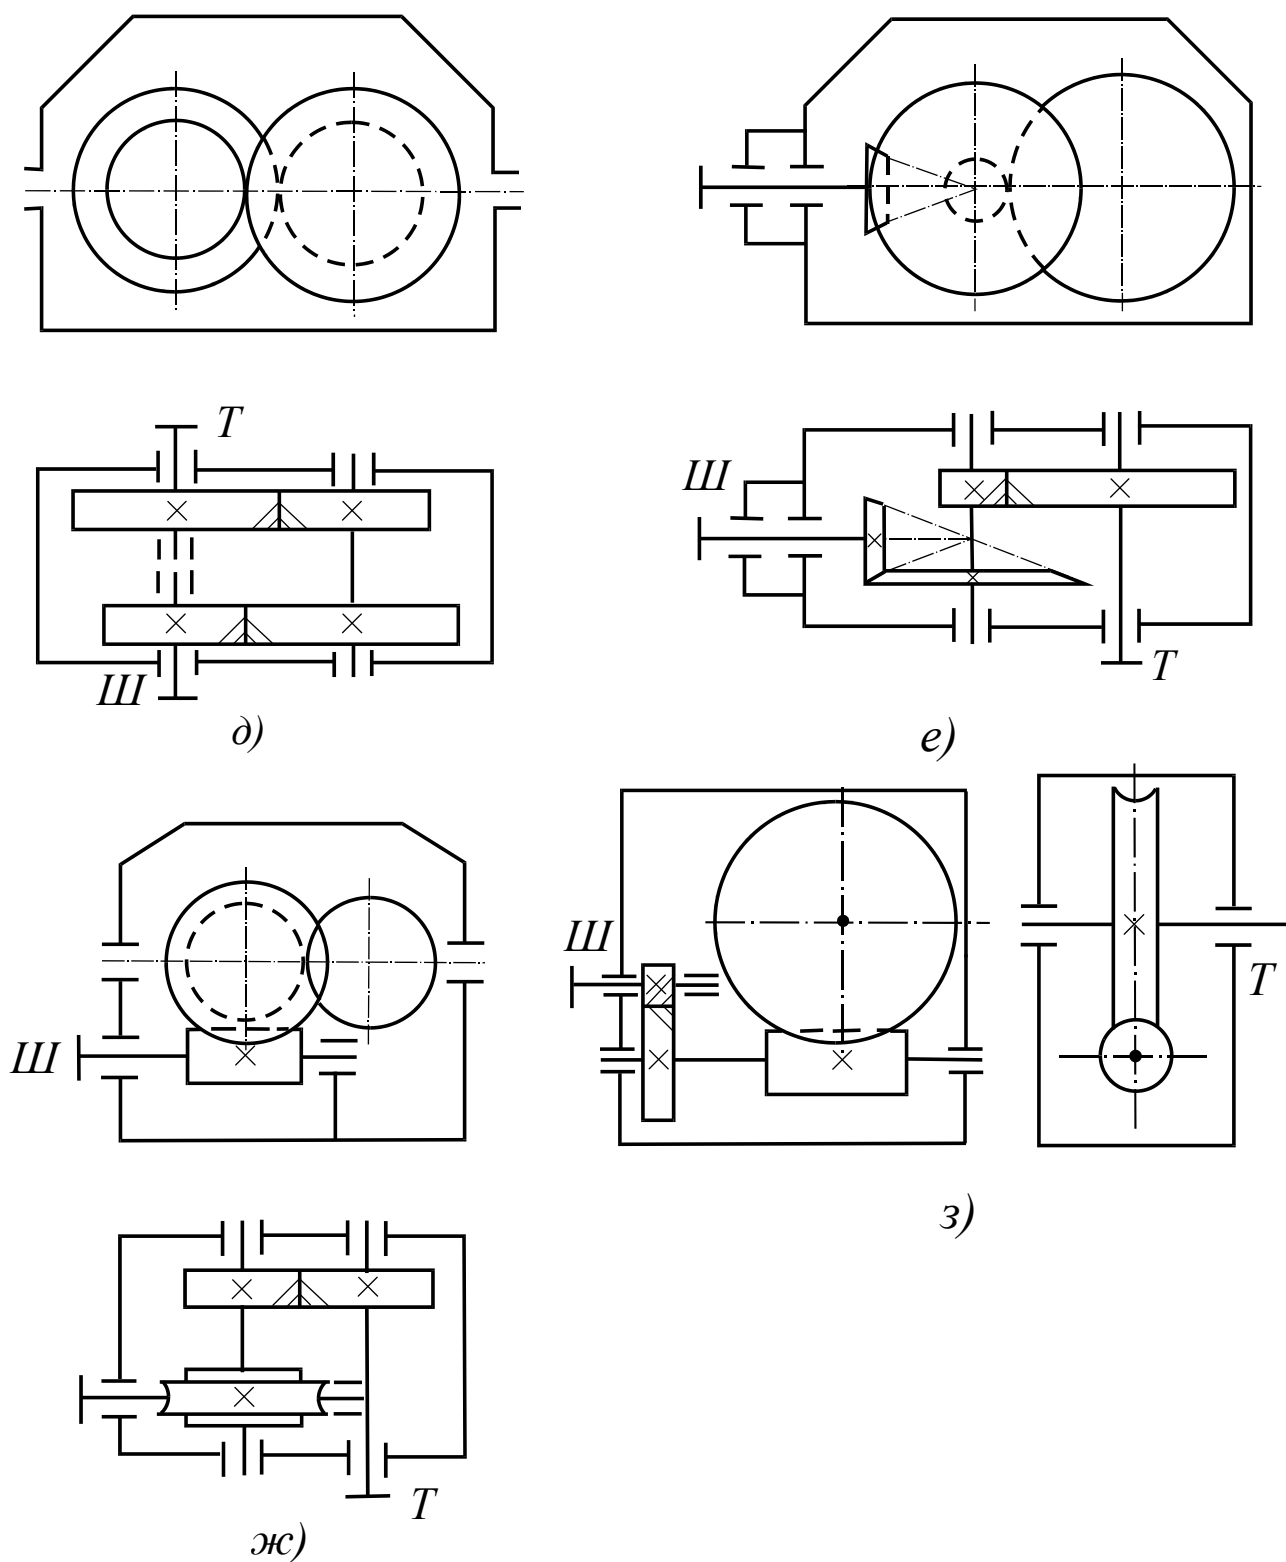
Кинематические схемы двухступенчатых редукторов
